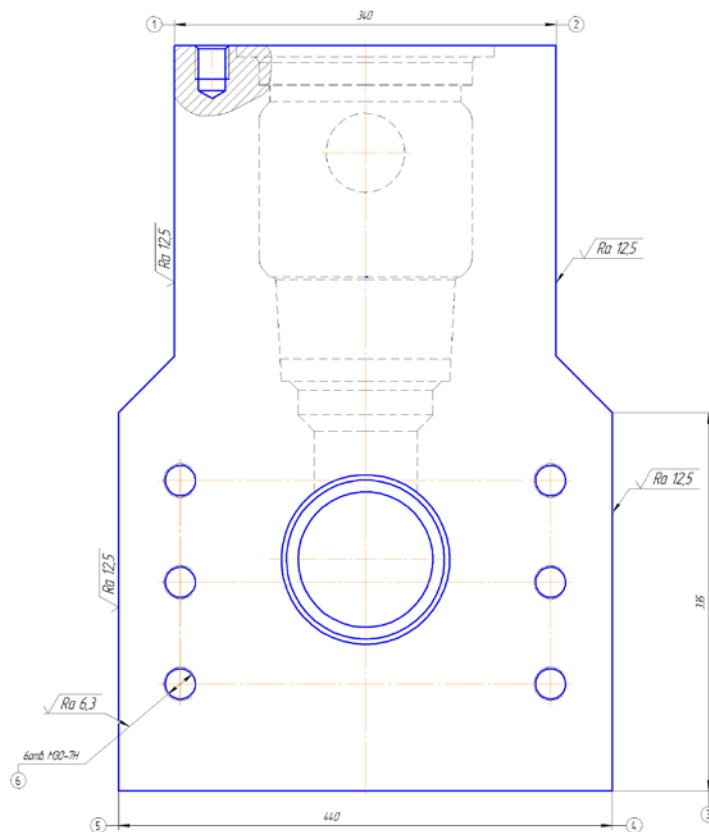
Эскиз детали «Коробка гидравлическая»
